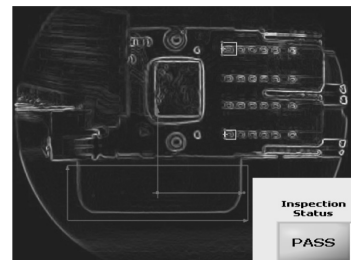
ระยะทางระหว่างเส้นตรงอ้างอิงกับแนวเส้นตรงของ Solder head pad ทั้งสองชุด
